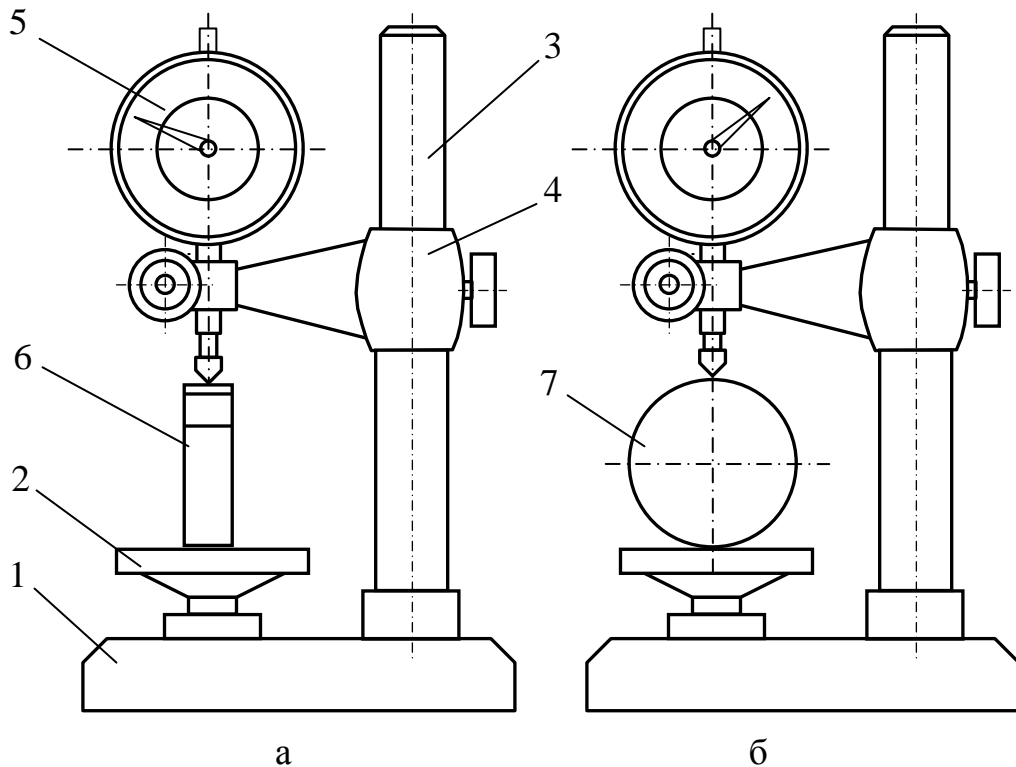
Схема настройки измерительного прибора на эталонной размер (а) и установки детали (б): 1 – основание штатива; 2 – предметный столик; 3 – стойка; 4 – подвижная штанга; 5 – индикаторная головка; 6 – блок концевых мер длины; 7 – измеряемая деталь
